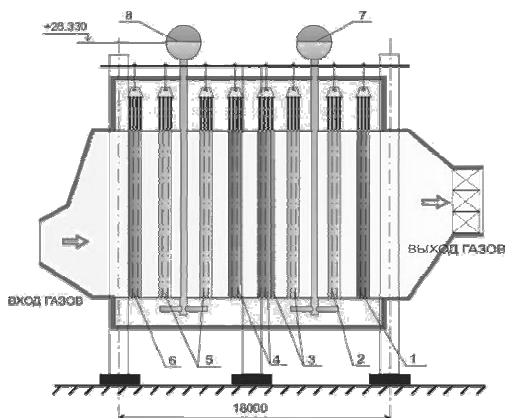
Горизонтальный КУ: 1 – газовый подогреватель конденсата; 2 – испарительный пакет низкого давления; 3 – пароперегреватель низкого давления; 4 – экономайзер высокого давления; 5 – испаритель высокого давления; 6 – пароперегреватель высокого давления; 7 – барабан контура низкого давления; 8 – барабан контура высокого давления
